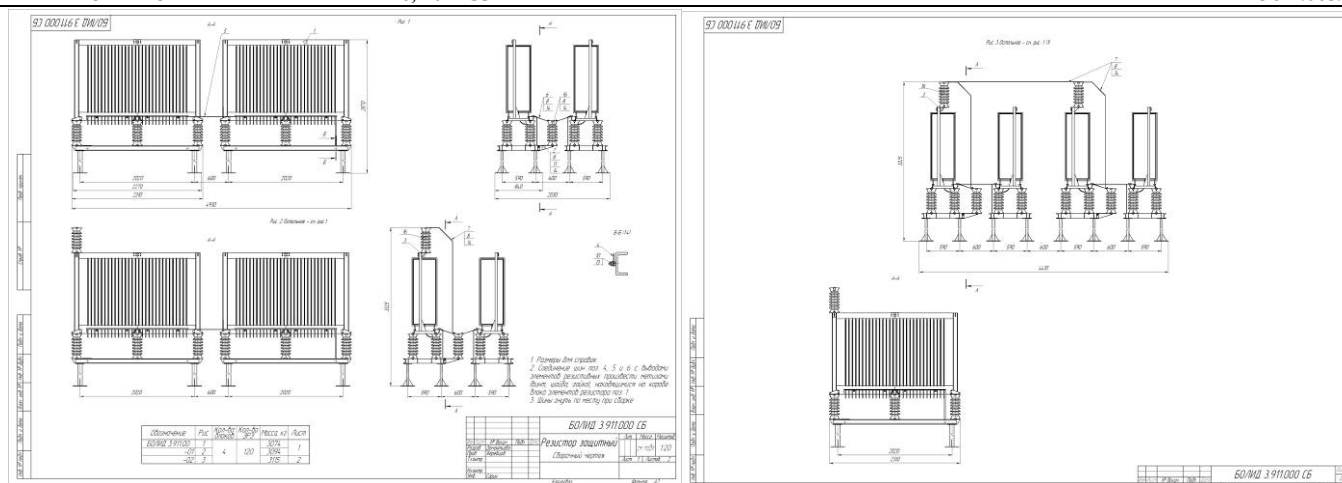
Резистор типа РЗ по чертежу БОЛИД 3.908.000
